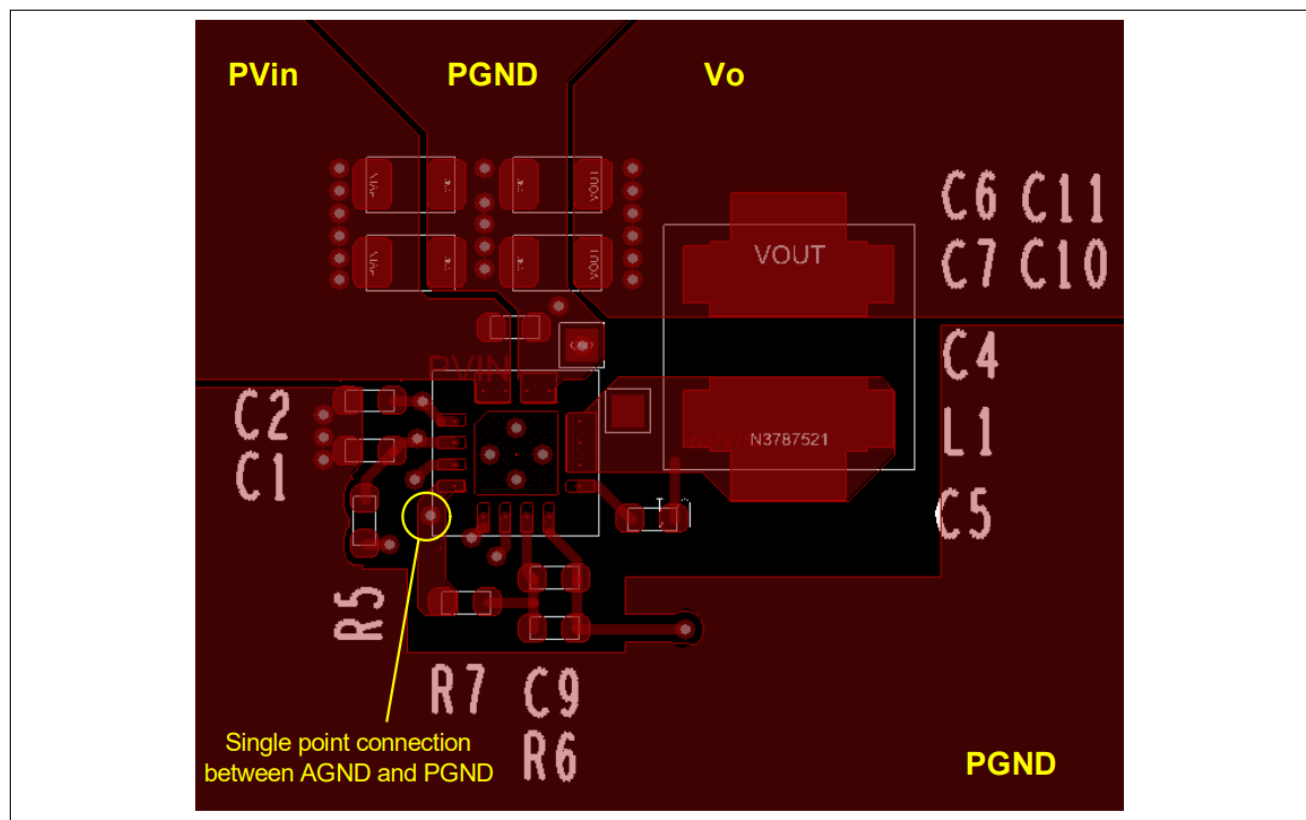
IRDC3883 Demo Board Layout – Top Layer
